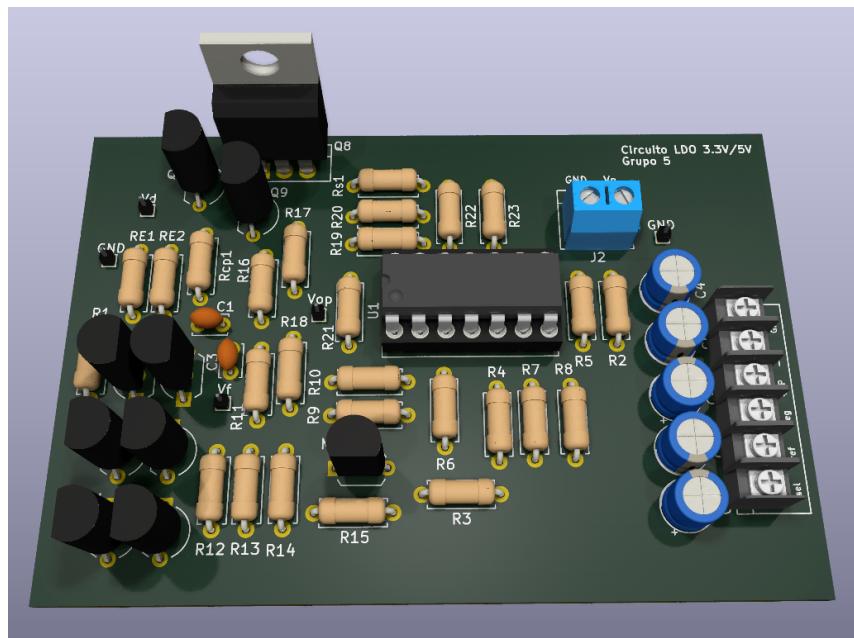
Render 3D* de la capa superior con los componentes del PCB del LDO.
